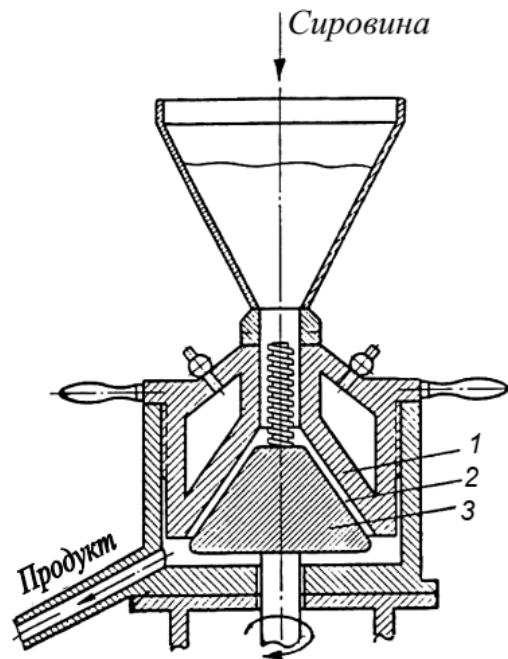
Схема колоїдного млина: 1 – статор; 2 – зазор; 3 – ротор
